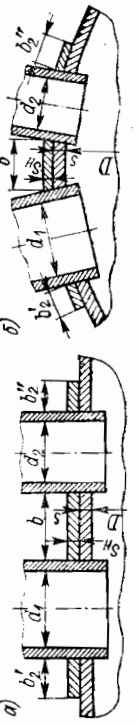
Конструкции совместного укрепления близкорасположенных отверстий для штуцеров: а — при расположении отверстий по образующей цилиндрической или конической стенок, б — при расположении отверстий в выпуклых днах или по окружности цилиндрической стенки
